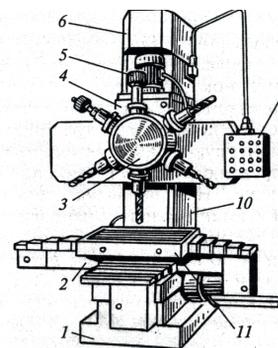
Расположение револьверной головки на сверлильном станке с ЧПУ
